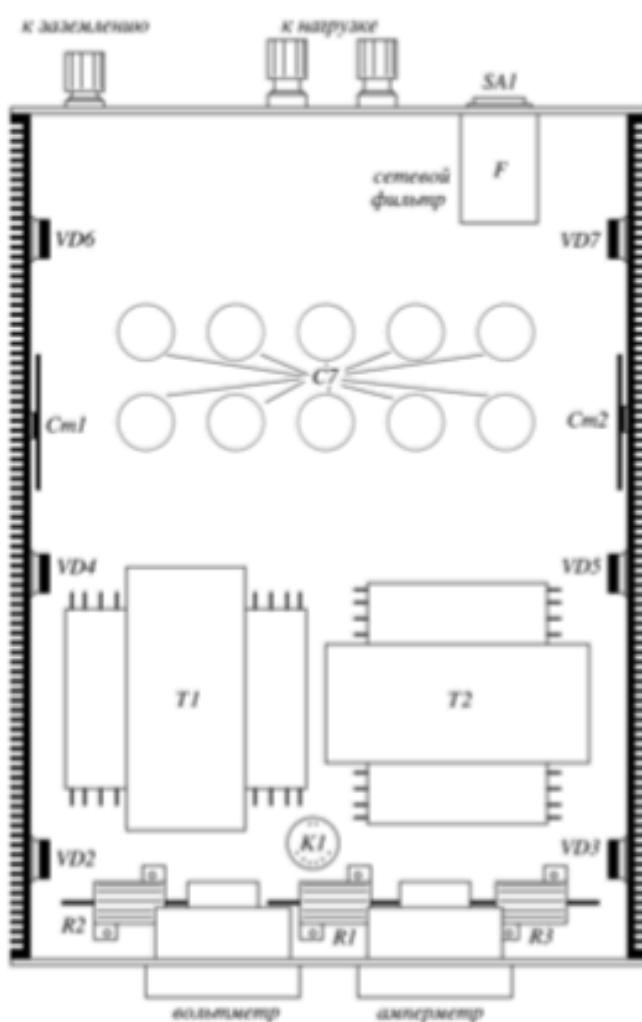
Эскиз расположения основных деталей в корпусе БП. Внутренние размеры корпуса: 327x232x135 мм. Конденсатор С7 набран из отдельных конденсаторов 10000 мкФ x 25...35 В. Свободное расположение деталей способствует применению конденсаторов старых конструкций с большими размерами и меньшему нагреву конденсаторов, что повышает их срок службы. В свободных местах корпуса могут быть размещены дополнительные детали стабилизаторов, о которых упомянуто в тексте статьи
